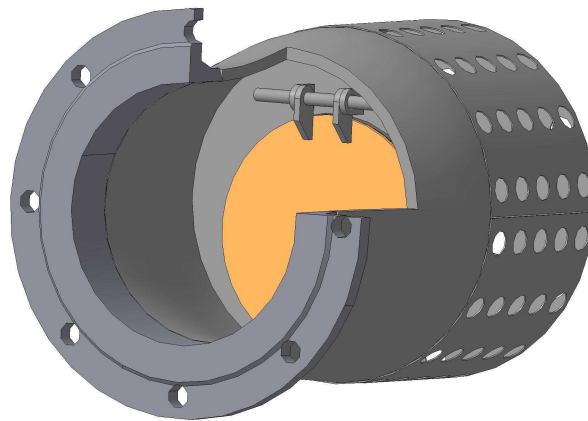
Клапан зворотний приймальний 16ч42р
